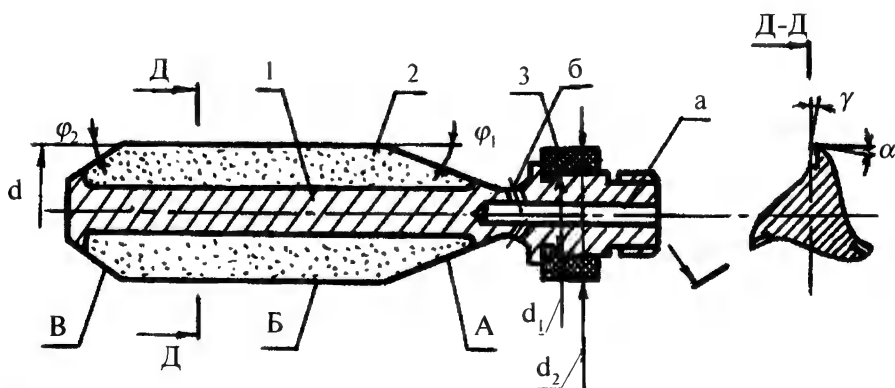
Развертка для скоростного глубокого развертывания: 1 - корпус, 2 - твердосплавной зуб, 3 - направляющая втулка.
